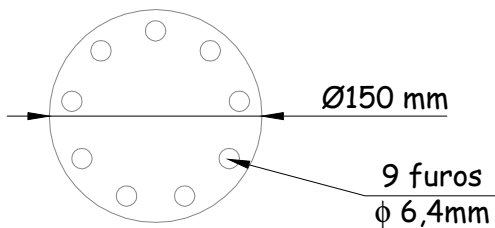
Detalhe da placa perfurada do sistema drenante
